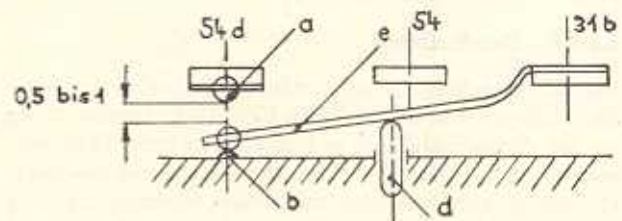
Ansicht von hinten gegen die Anschlußplatte mit Endausschalter
